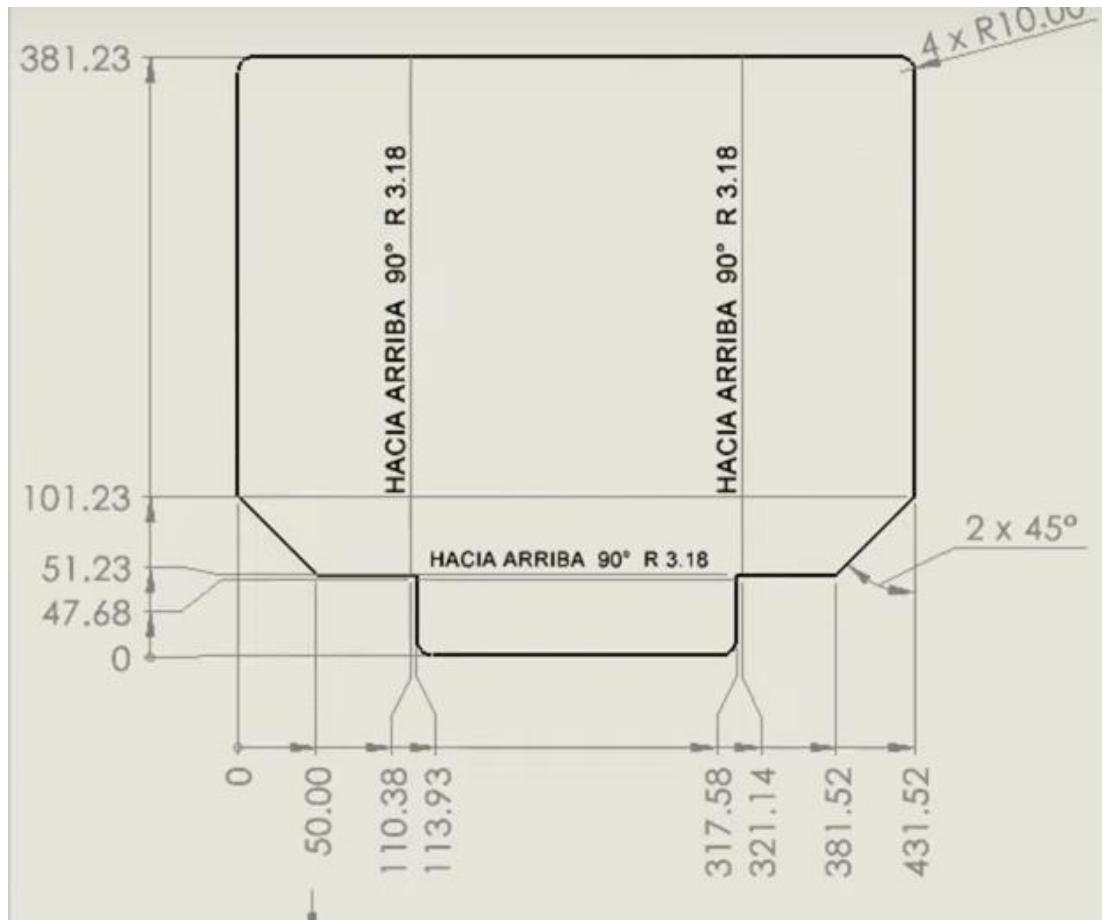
Pieza fabricada con chapa de acero inoxidable de 2,7mm de espesor. Fuente: Diseño Mecánico JC.
